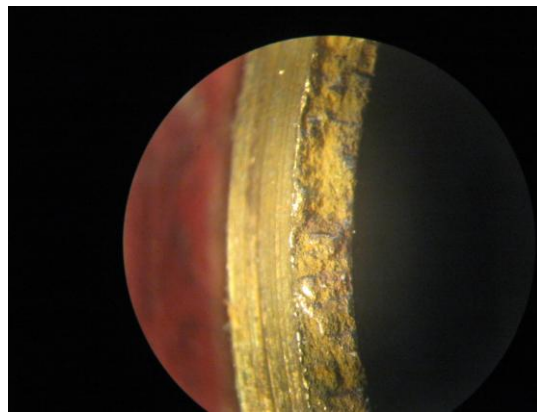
Поверхня злому різьбового з'єднання з шлаковими і неметалевими включеннями, що вкривають всю поверхню. Злом не має характерного для металу блиску
